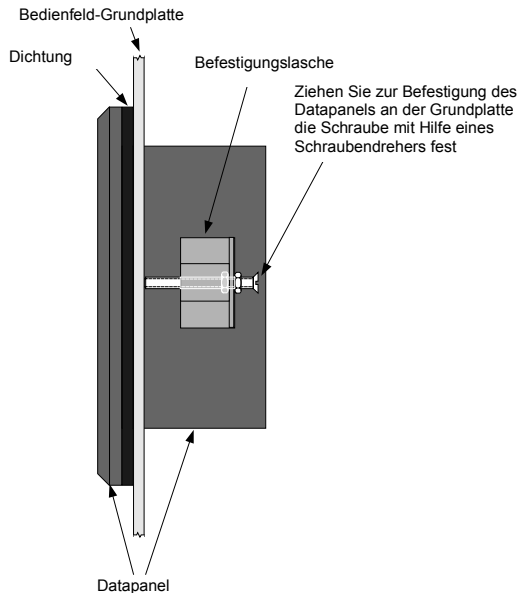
Datapanel-Befestigung, Seitenansicht
